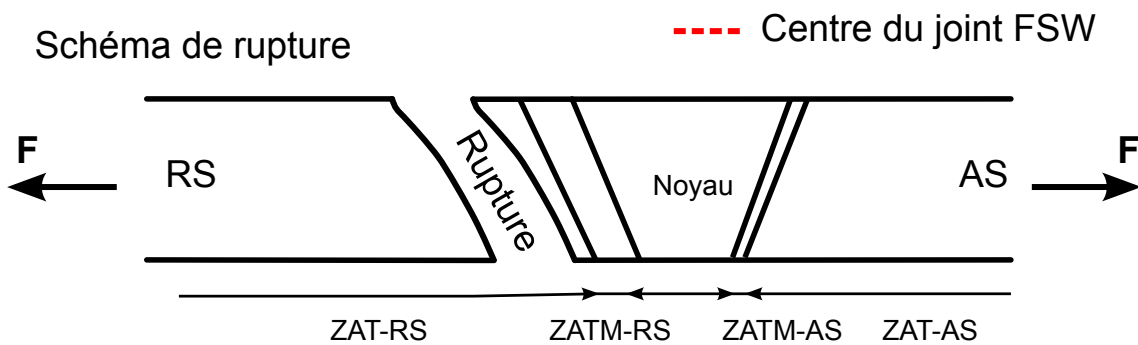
Rupture des joints soudés par FSW en alliage d'aluminium 7449-T79 sous chargement de traction monotone quasi-statique
